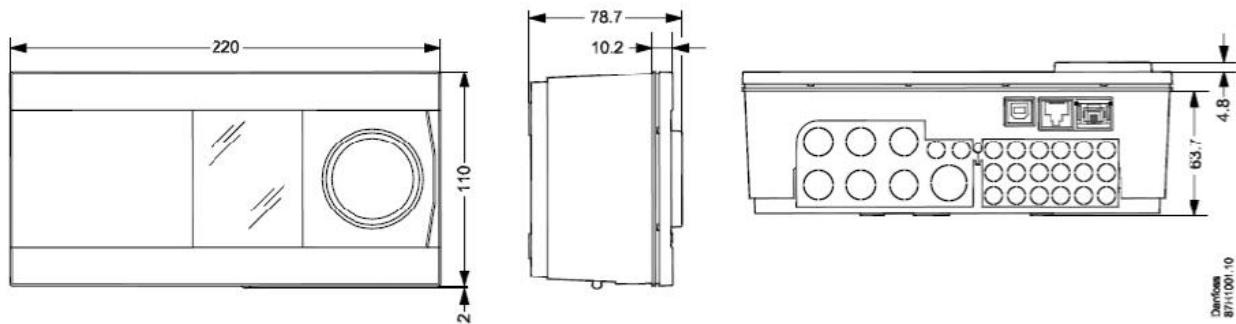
Габаритные и присоединительные размеры ECL Comfort 310.
